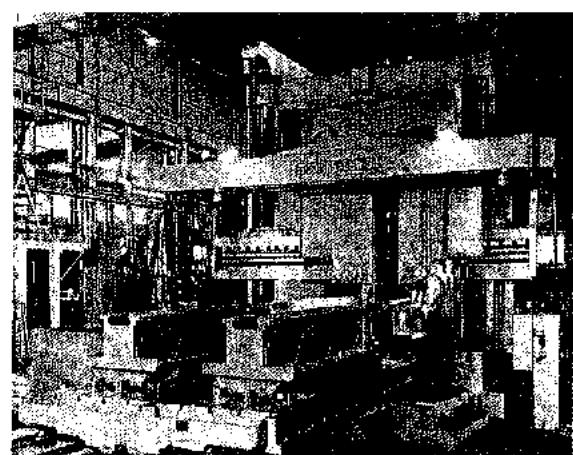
Fresadora tipo planeadora (Giddings & Lewis Machine Tool Co.)
